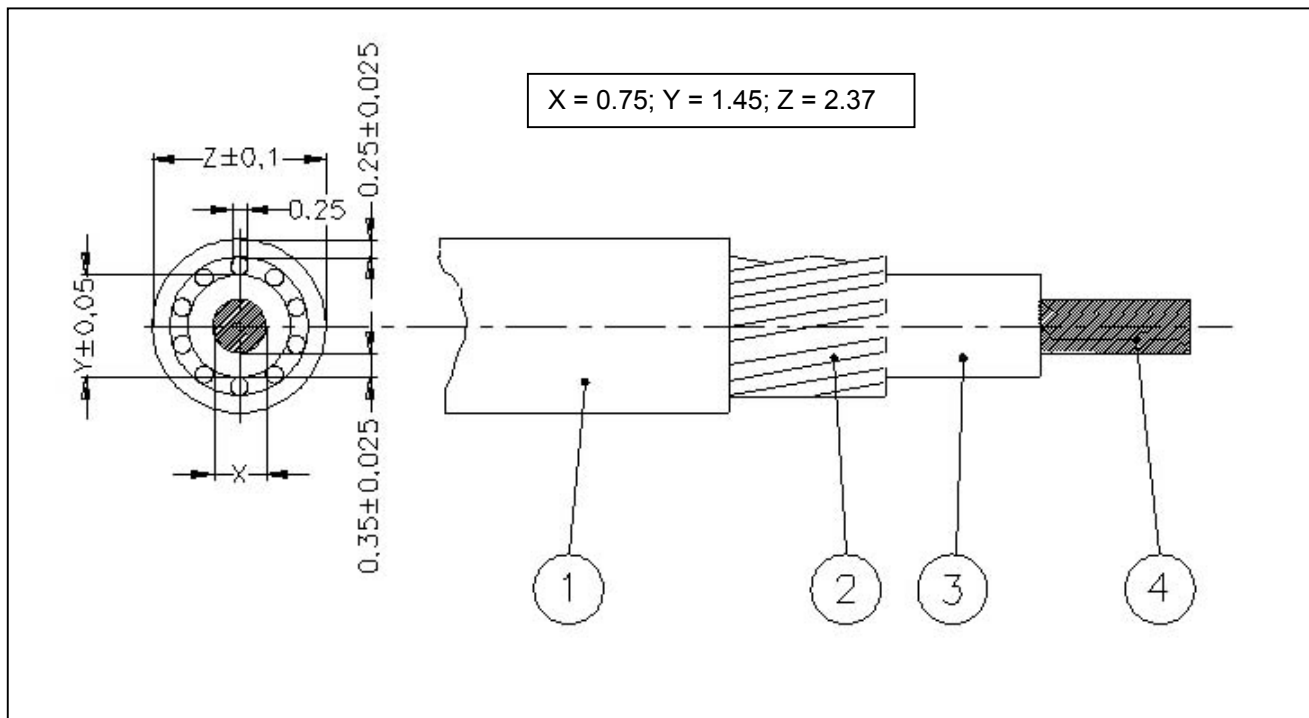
Устройство нагревательного кабеля для матов devimat™ DSVF-100, DSVF-150.
